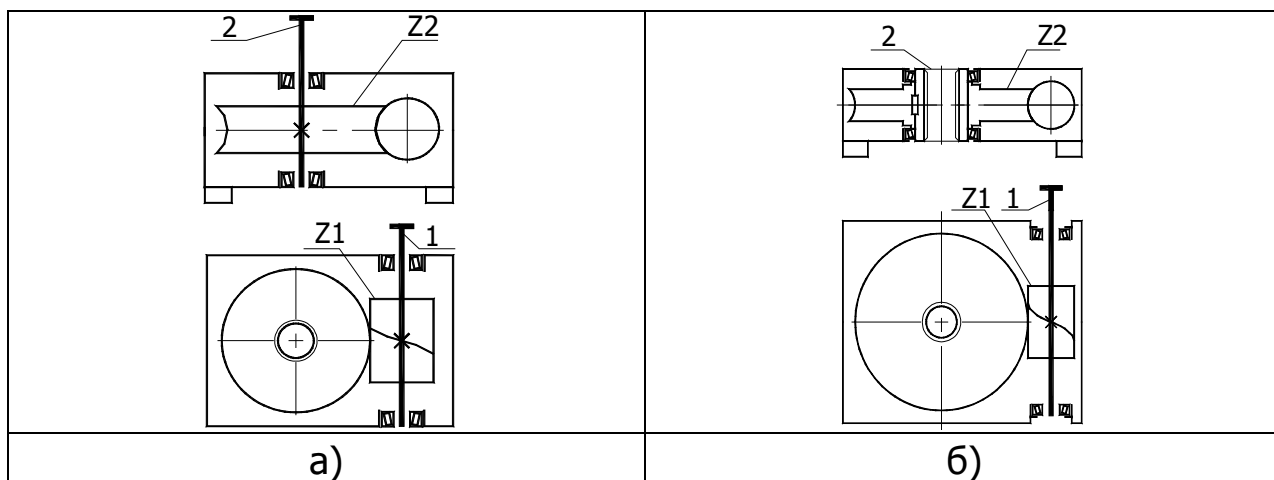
Схемы червячных редукторов с вертикальным валом колеса. Для привода рабочих органов с вертикальными валами: планшайбы карусельных станков и роторных конвейеров, смесители, дробилки, звездочки подвесных конвейеров, механические винтовые домкраты, затворы трубопроводов большого диаметра.
